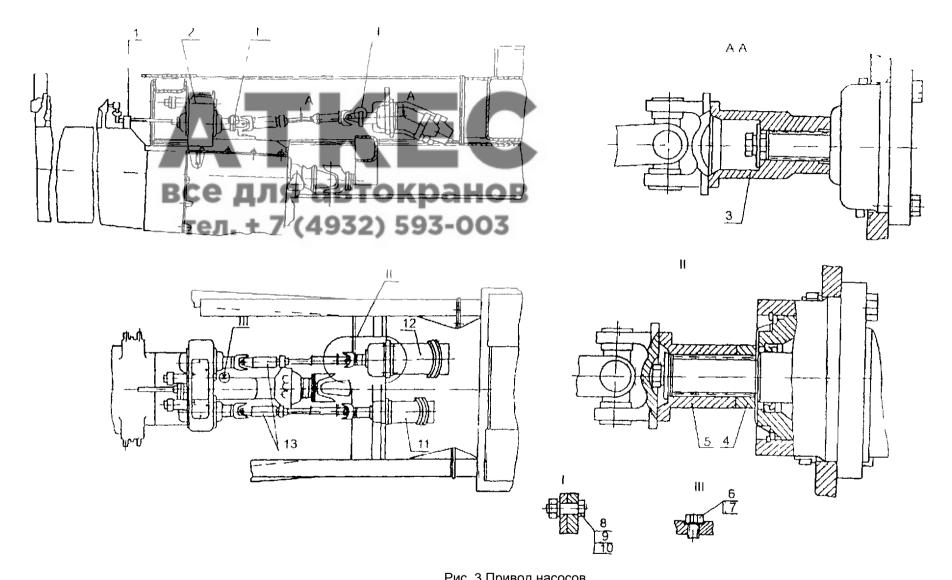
Привод насосов 1 - сферическая опора 2 - коробка отбора мощности (КОМ), 3, 5 - фланцы 4 – кольцо; 6 – пробка; 7, 10 шайбы; 8 – болт; 9 - гайка, 11, 12-насосы, 13 - карданный вал
